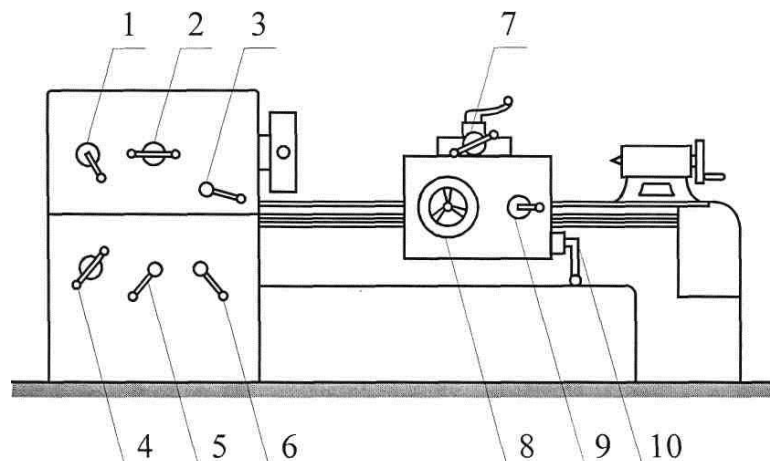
Органы управления станка 1М61. 1 - рукоятка установки нормального или увеличенного шага резьбы и реверсирования вращения ходового винта; 2- рукоятка установки числа оборотов шпинделя; 3 - рукоятка установки чисел оборотов (перебор); 4 - установка величины подачи; 5 - установка шага резьбы; 6 - включение ходового винта или ходового вала; 7 - маховичок поперечного перемещения суппорта; 8 - маховичок продольного перемещения суппорта; 9 - рукоятка включения маточной гайки; 10 - включение прямого или обратного вращения шпинделя.
